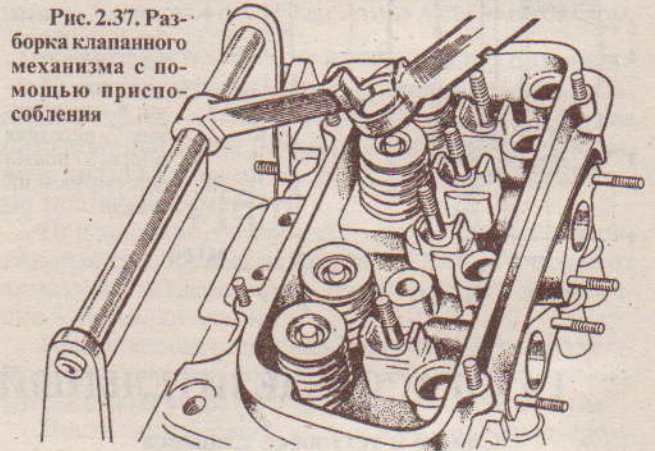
Разборка клапанного механизма с помощью приспособления
